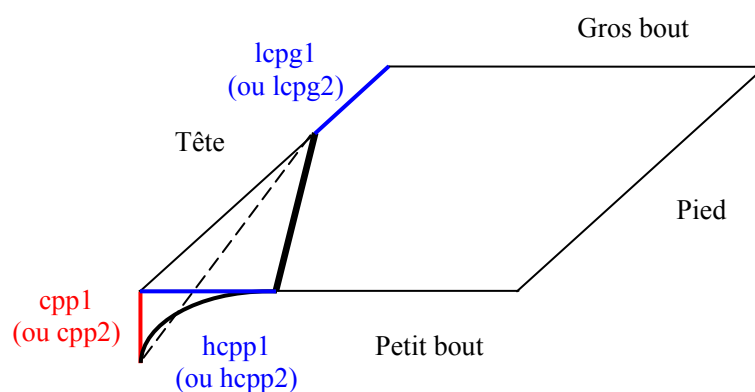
Correction de profil sur le pignon (ou sur la roue) sur le petit bout seulement
